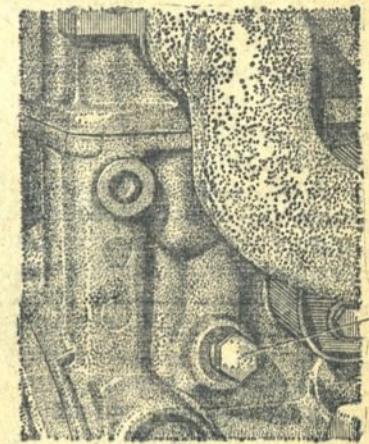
Пробка сливного отверстия на стенке рубашки блока цилиндров;
